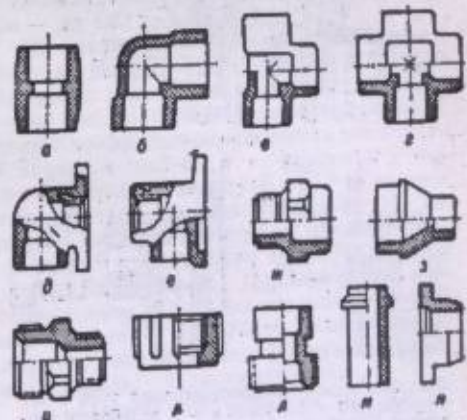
Пластмассовые фасонные части: а — муфта; б — угольник; в — тройник; г — крестовина; д — угольник с крепежным фланцем, тип А; е — то же, тип Б; ж — футорка; з — переход; и — вилка; к — гайка напильная; л — втулка резьбовая; м — втулка под фланец.
